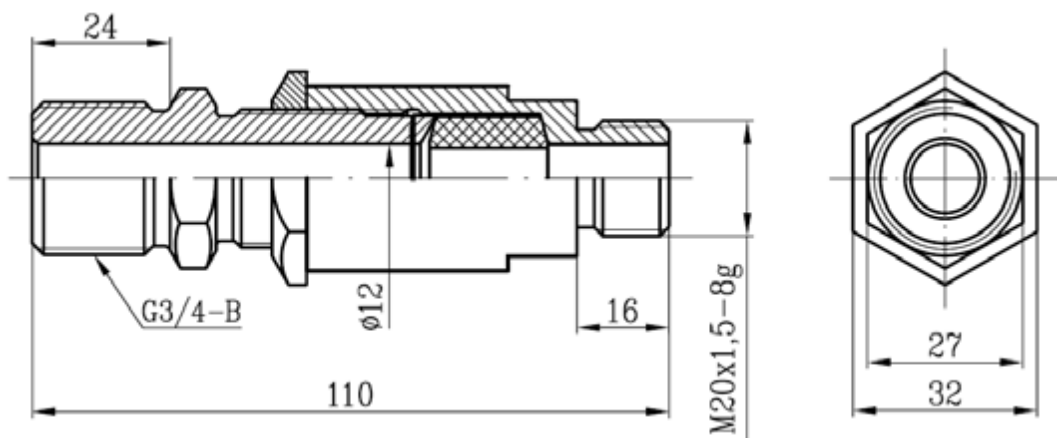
Ввод кабельный для трубного монтажа (ТБ 3/4")
